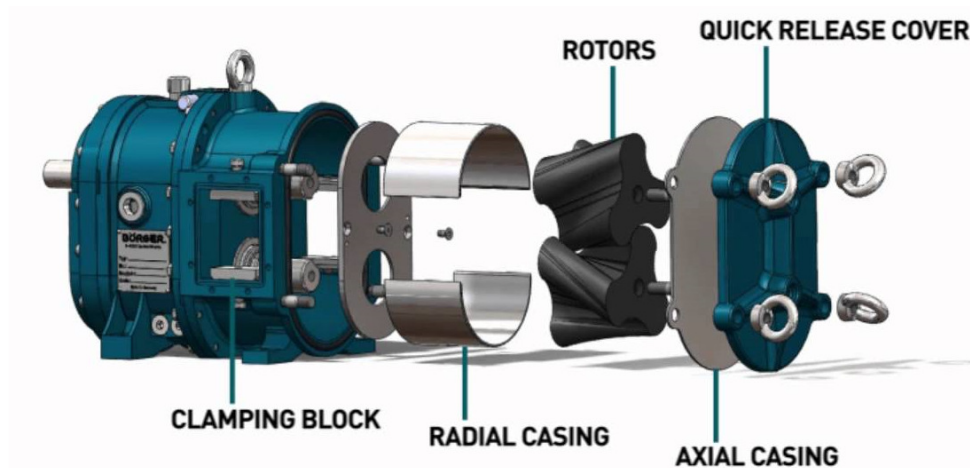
Desenho de conjunto de bomba de glóbulos [15]
